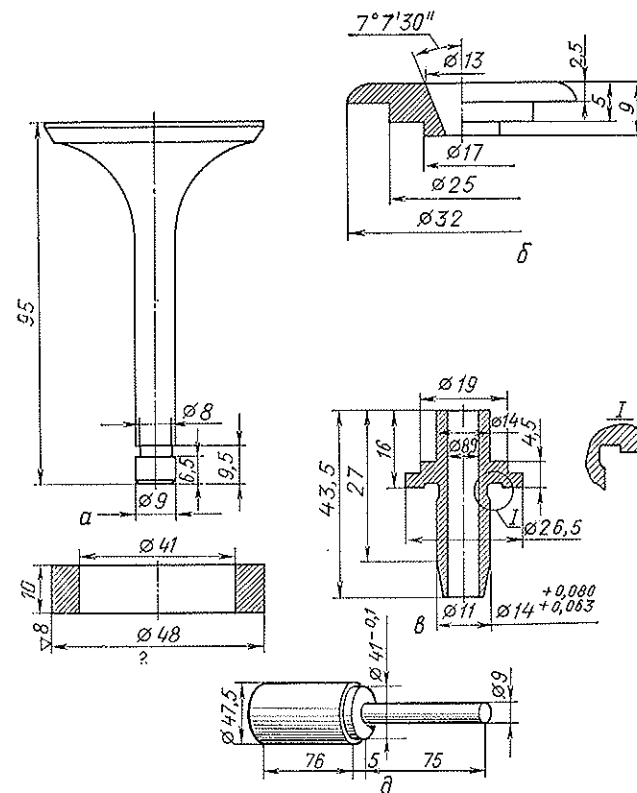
Детали узла впускного клапана двигателя Д-3 и оправка:
